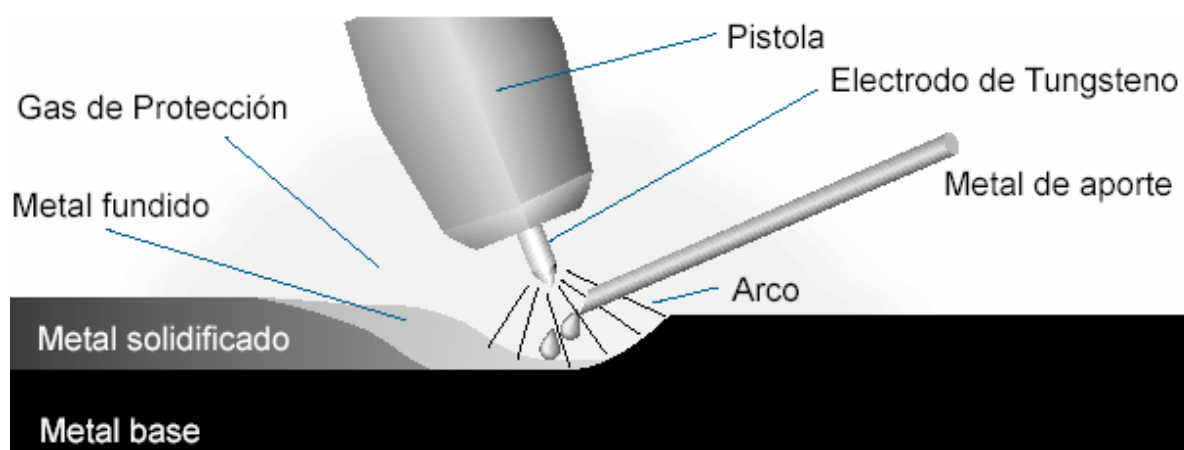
Soldadura de arco con electrodo de tungsteno y protección de gas.
